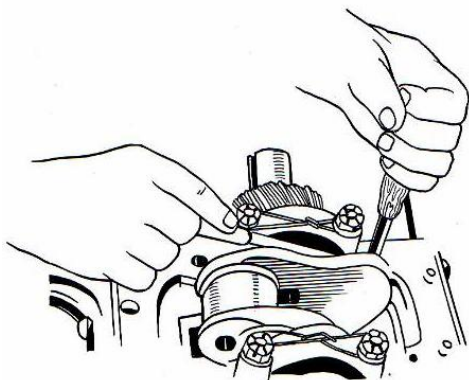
Проверка осевого люфта коленчатого вала щупом
